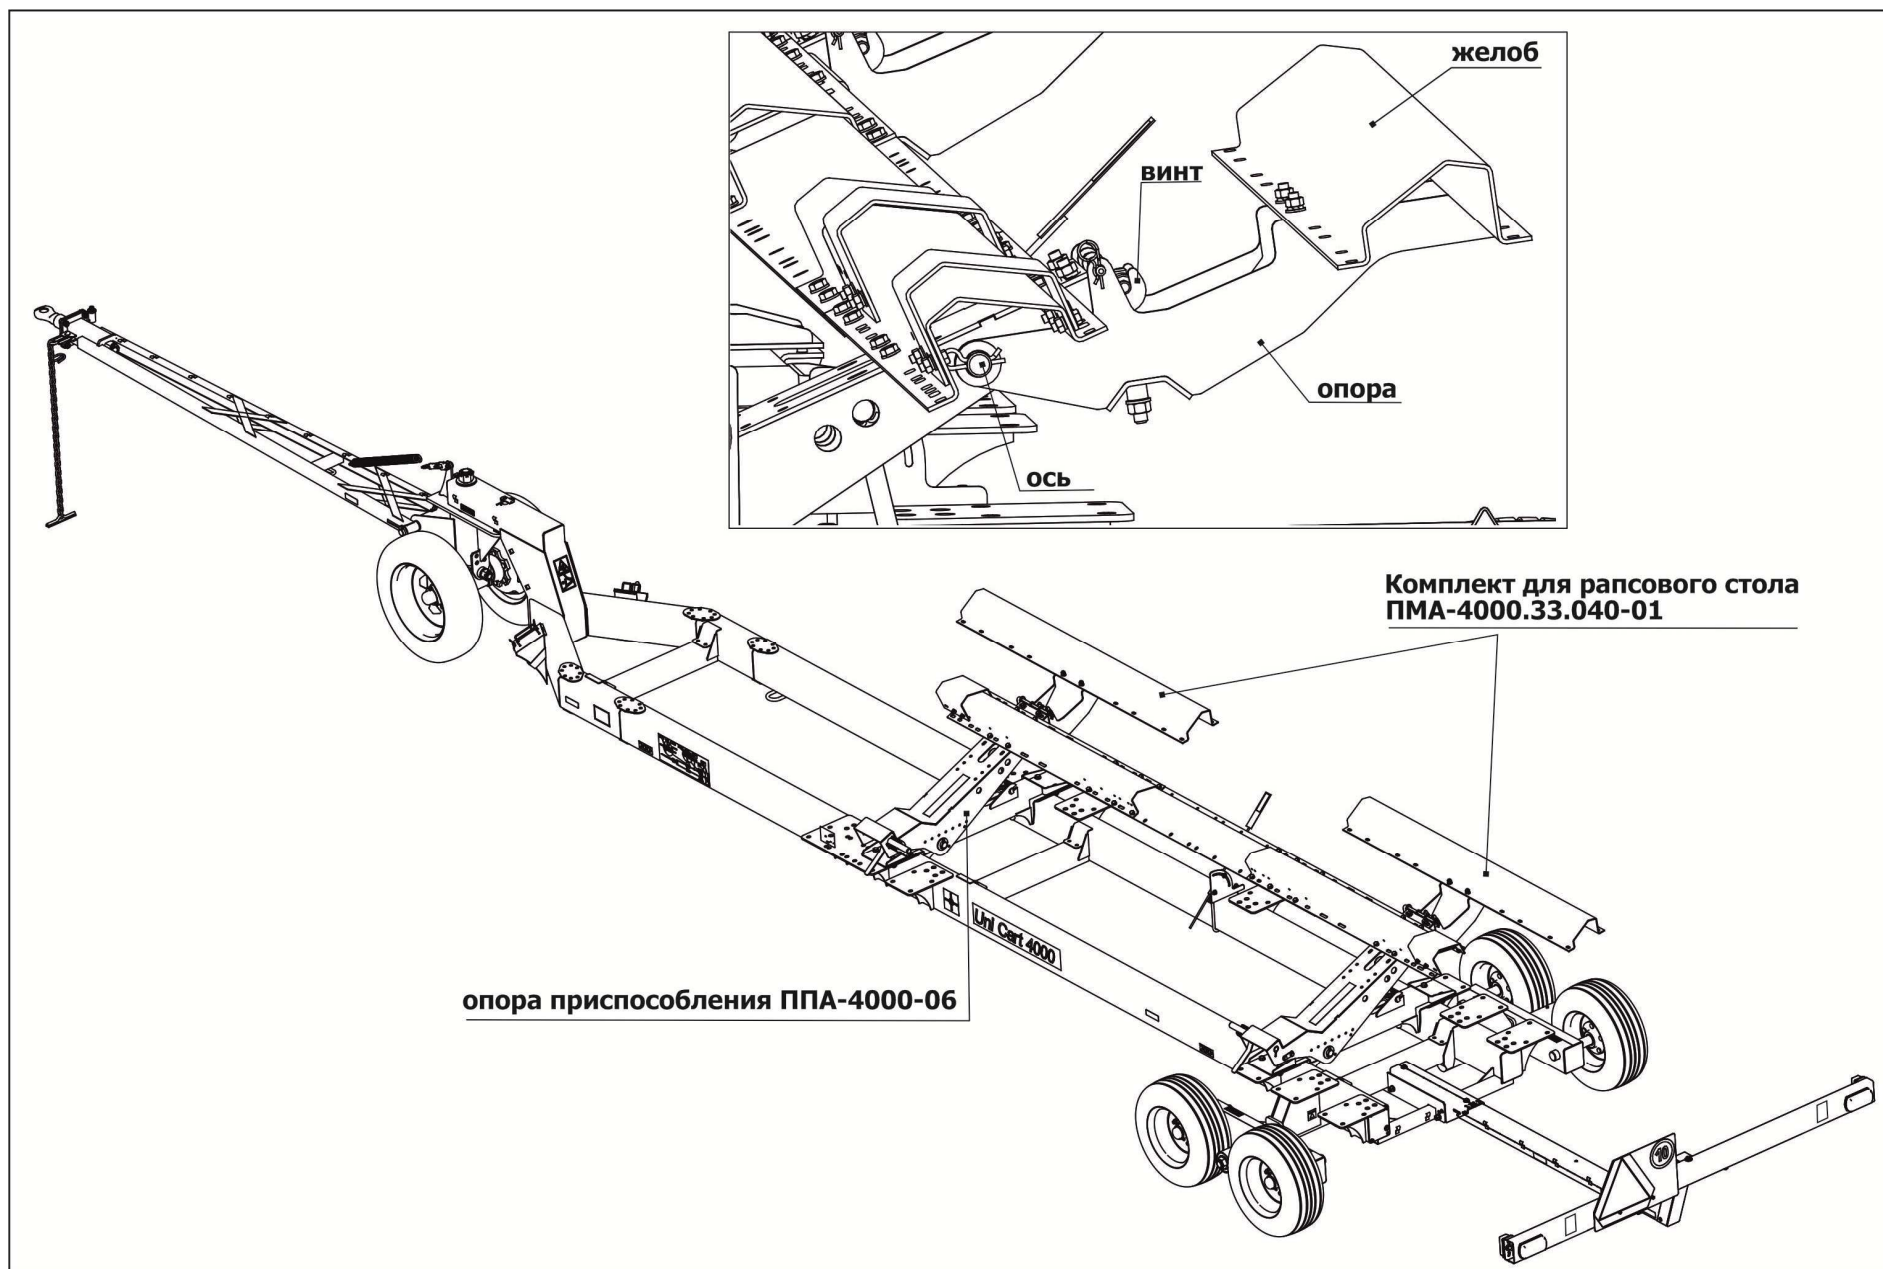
Установка комплекта для рапсового стола ПМА-4000.33.040-01 на приспособление ППА-4000-06
